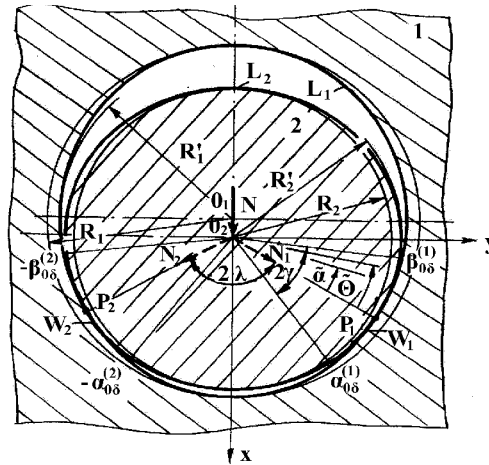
Розрахункова схема підшипника ковзання з овальністю вала та коловою втулкою
